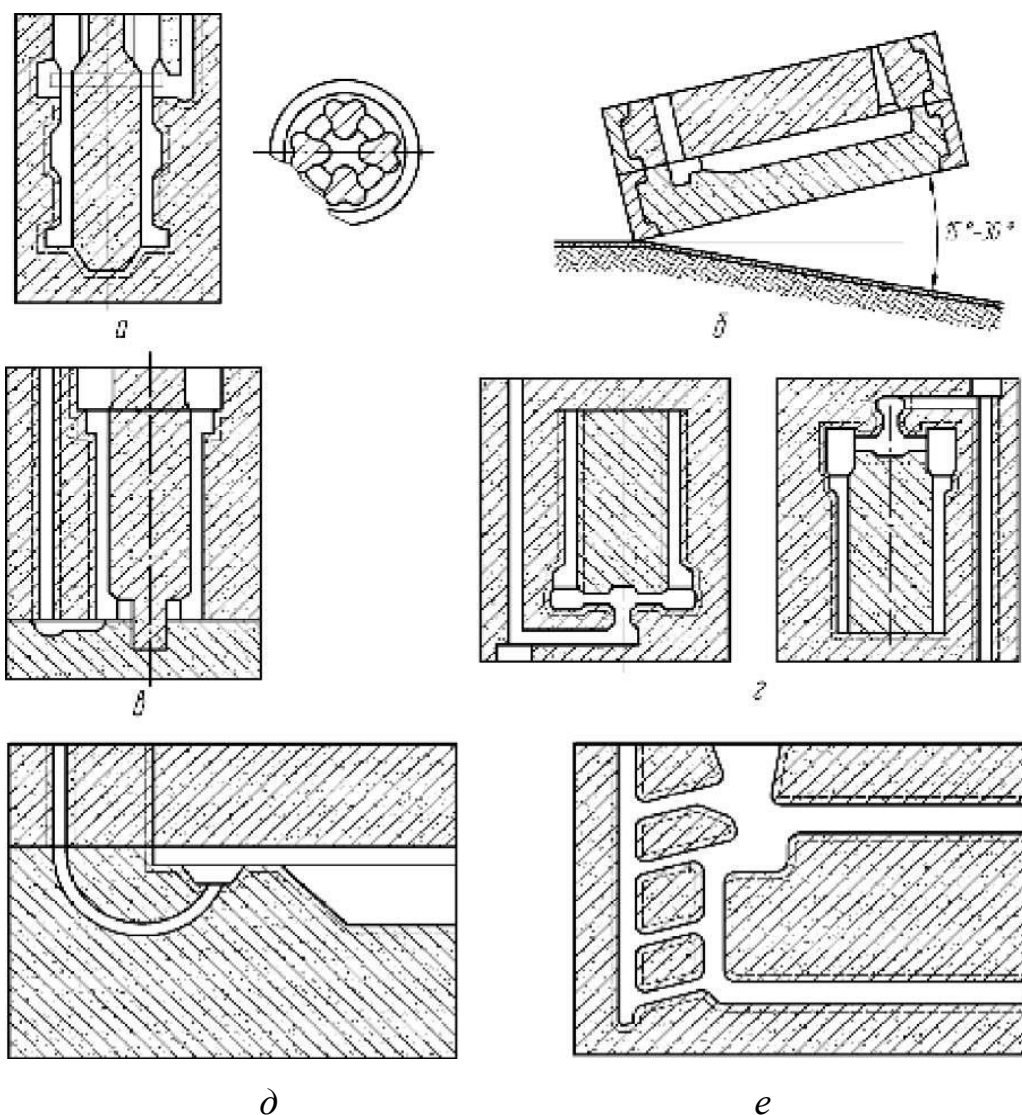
Типовые конструкции литниковых систем для стальных отливок
